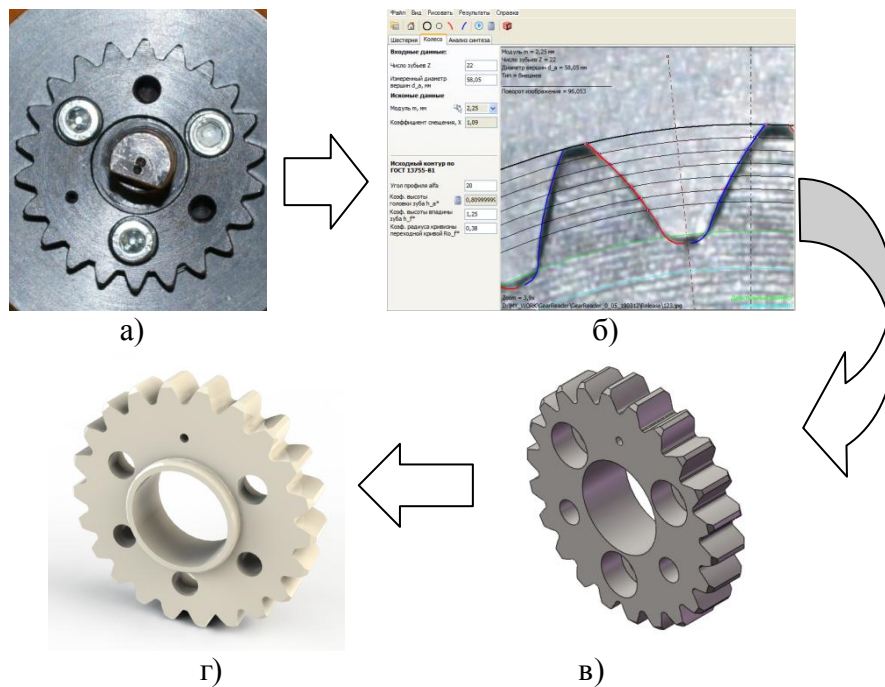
Условная схема обратного проектирования зубчатой передачи: а – фотография металлической шестерни; б – анализ фотографии ($m = 2,25$; $X = 1,09$); в – 3D модель; г – напечатанное готовое изделие.
